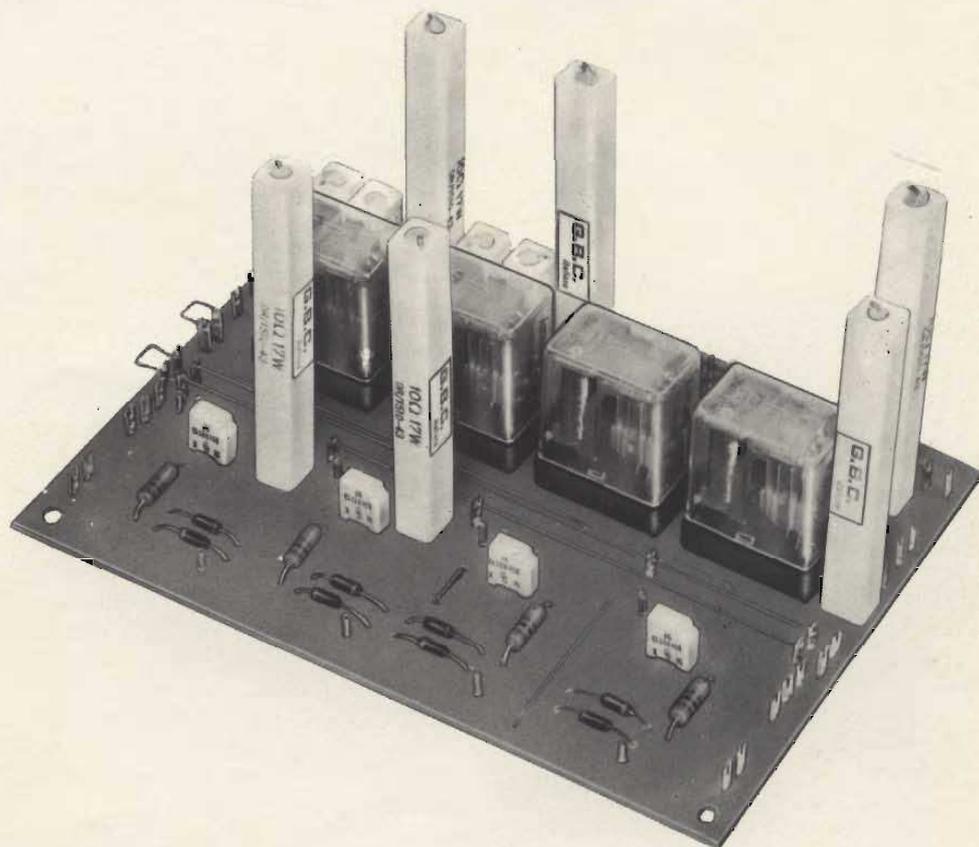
Aspetto della piastra a circuito stampato dell'UK 830 a montaggio ultimato.
